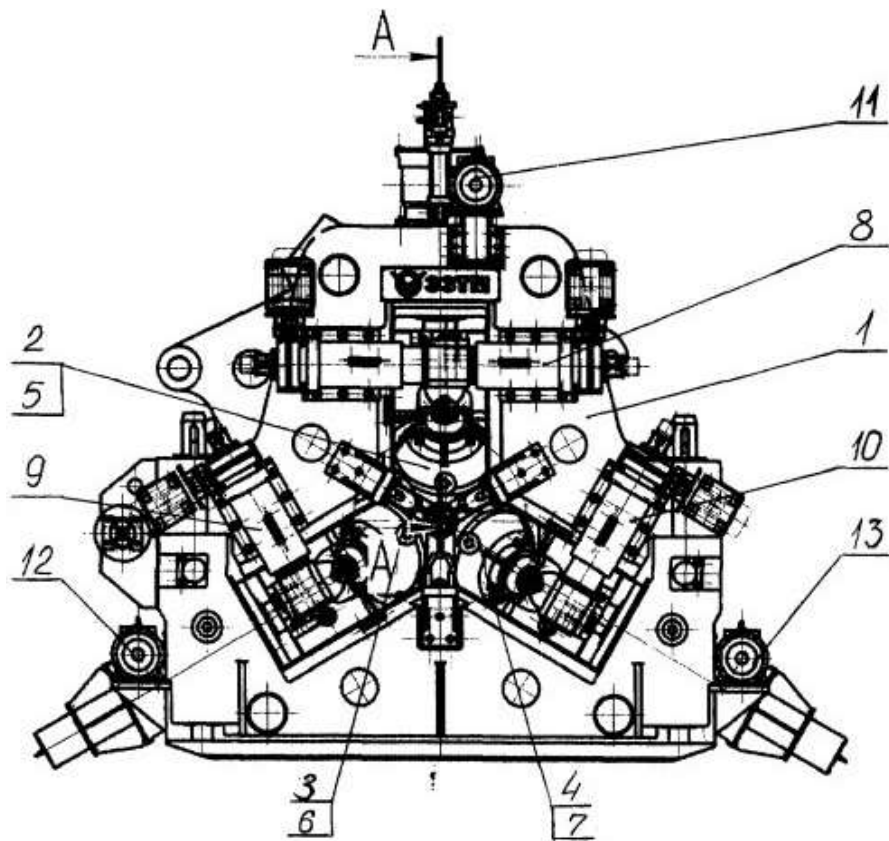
Рабочая клеть стана поперечно винтовой прокатки. Общий вид
